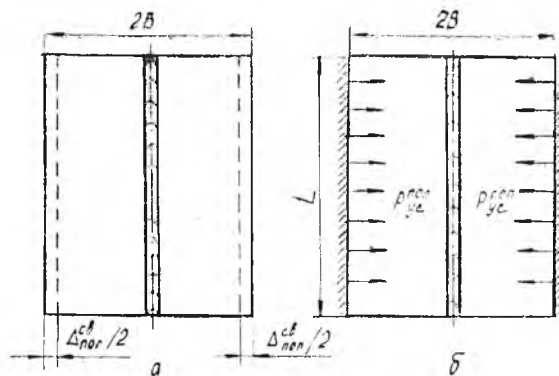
А. Поперечные деформации при сварке свободных пластин (а) и образование поперечной усадочной силы при сварке закрепленных пластин (б)
